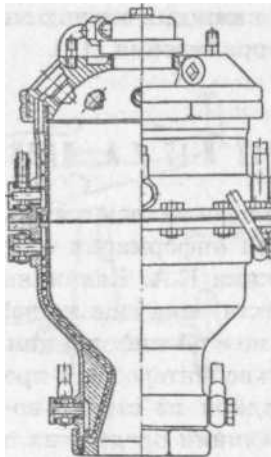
Жидкостный ракетный двигатель РДК-1—150 [12]
